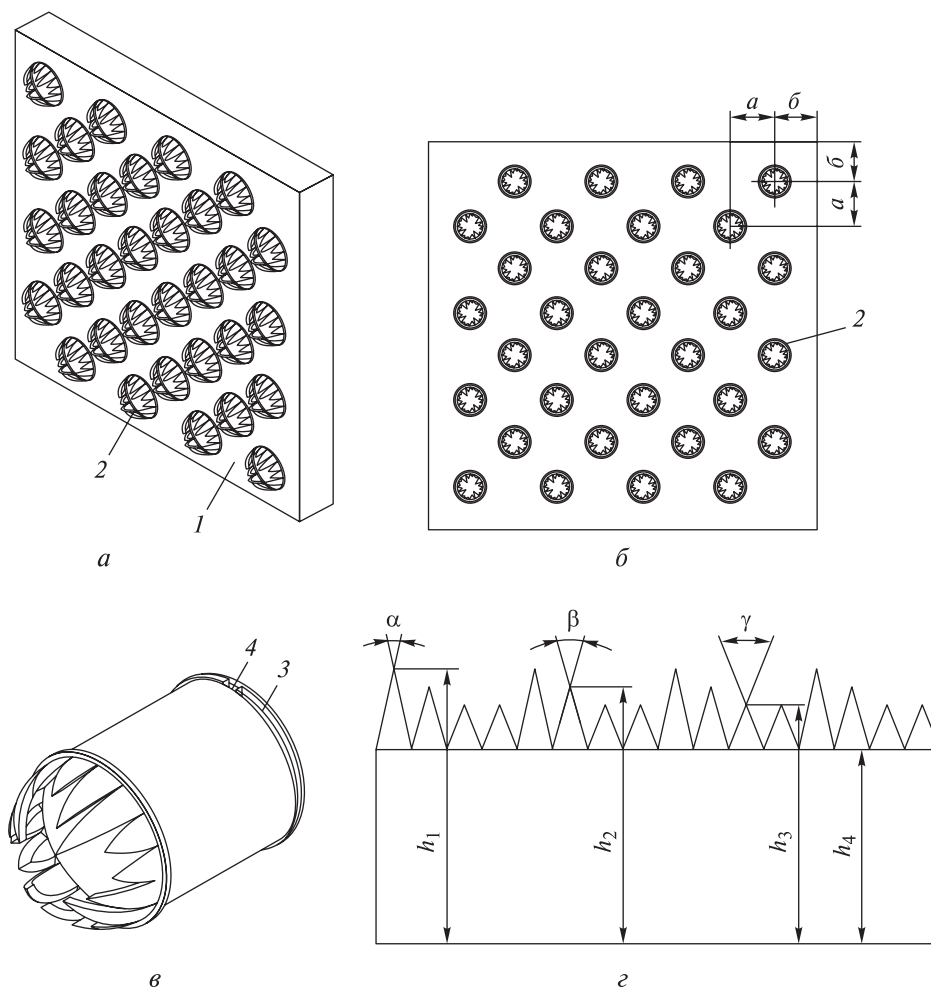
Устройство конструктивного элемента, позволяющего дополнительно фибриллировать поверхность древесного волокна: *a, б* — лопасти ротора с конструктивными элементами: соответственно 3D-модель и вид сзади; *в* — конструктивный элемент; *г* — развертка конструктивного элемента; *1* — лопасть ротора; *2* — конструктивный элемент; *3* — кольцо стопорное; *4* — паз для кольца стопорного; *высота зубьев*: h_1 — больших; h_2 — средних; h_3 — малых; h_4 — длина образующей конструктивного элемента; *углы при вершине зубьев*: α — больших; β — средних; γ — малых; a — расстояние между осями конструктивных элементов; b — расстояние между осями конструктивных элементов и краем лопасти ротора
